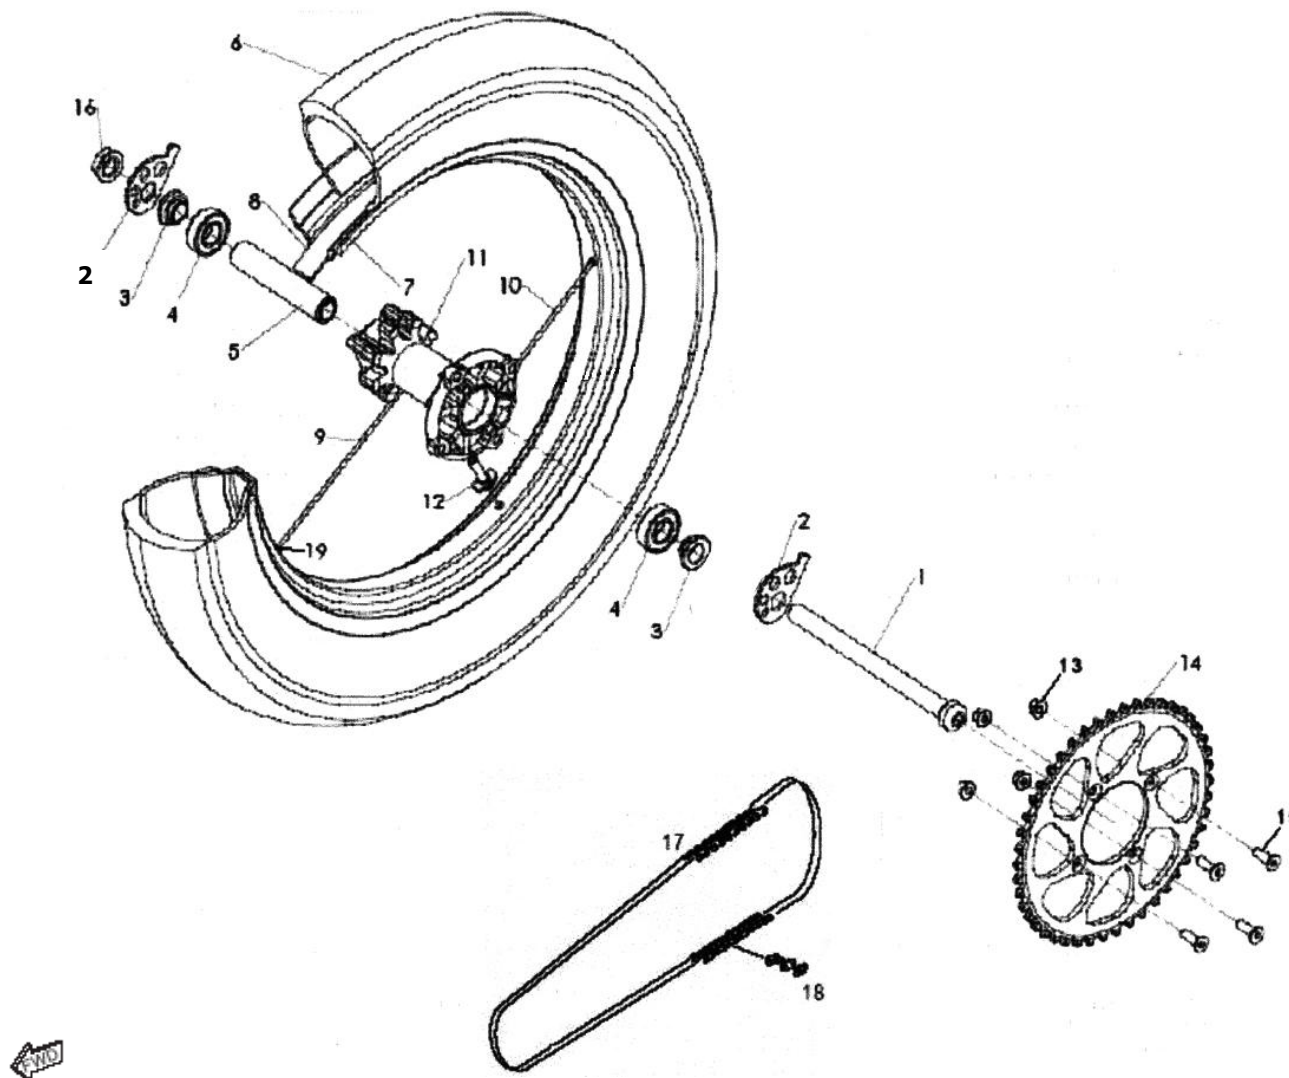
ROUE ARRIÈRE / REAR WHEEL / RUEDA TRASERA
